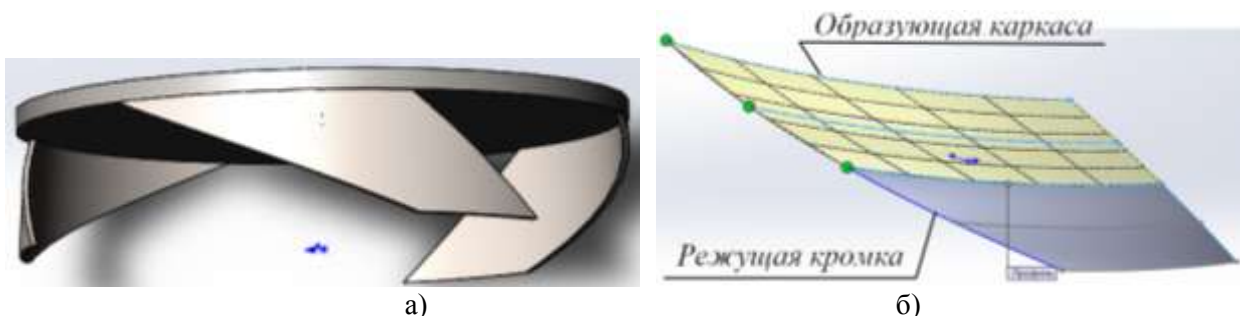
Формирование рабочей поверхности почвообрабатывающего элемента
